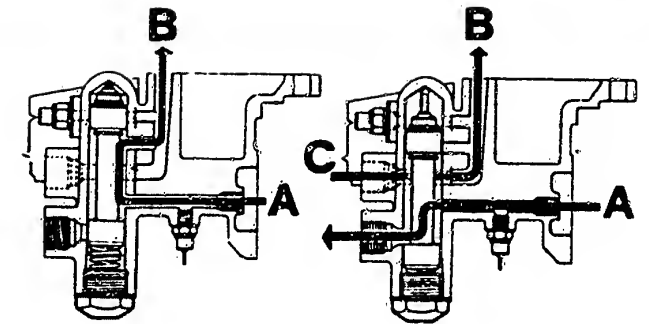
Schnitt durch das Thermostatgehäuse. A vom Ölfilter – B zu den Schmierstellen im Motor – C vom Ölkühler.
